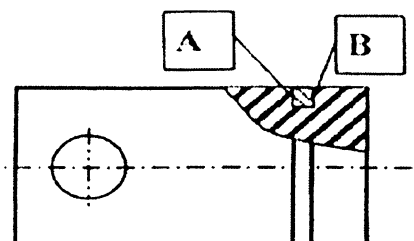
Поршень, контролируемый наличие качества сцепления нирезистовой вставки с алюминием: А и В — поверхности вставки
